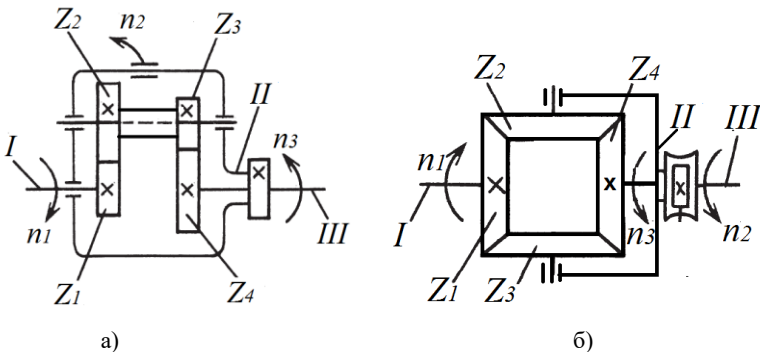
Диференціальні передачі: а – з циліндричними колесами; б – з конічними колесами
